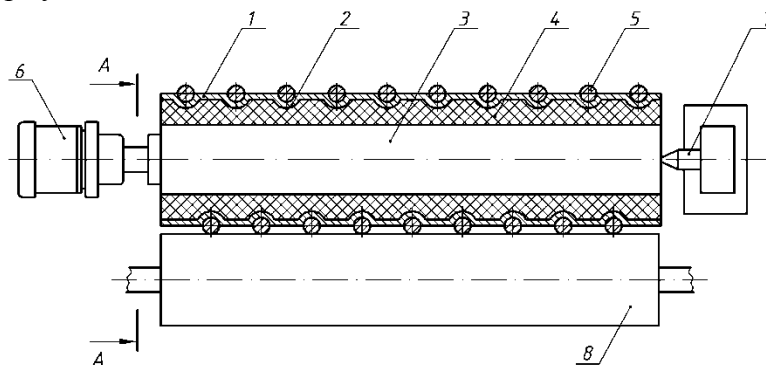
Конструктивна схема способу виготовлення гвинтових транспортних труб
